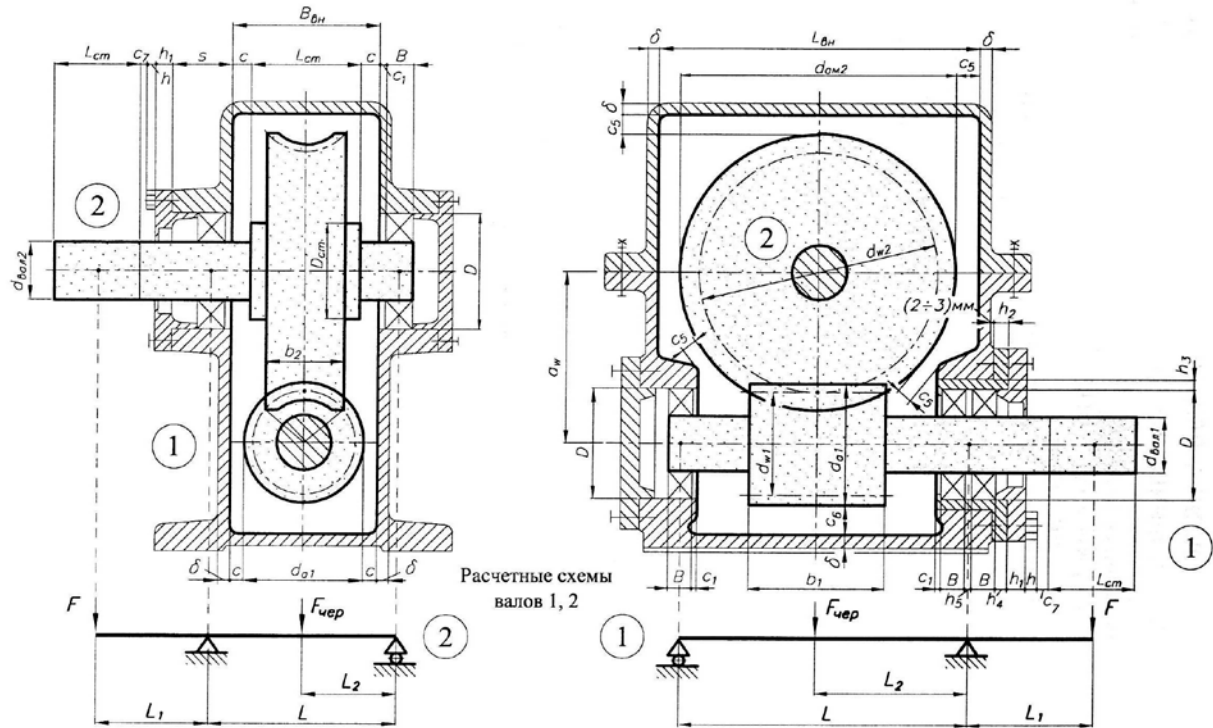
Схема компоновки одноступенчатого червячного редуктора
